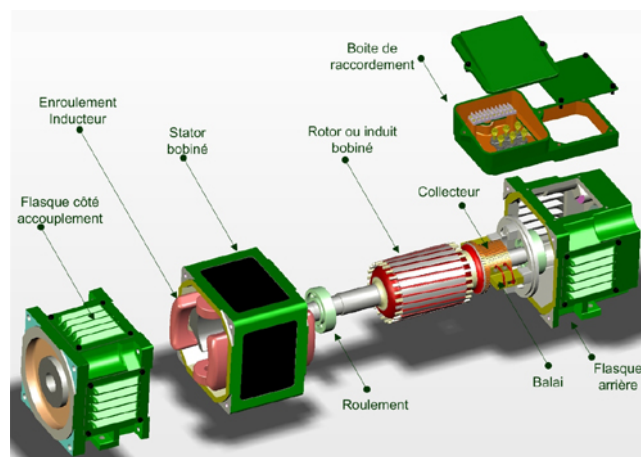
Vue éclatée d'une machine à courant continu
